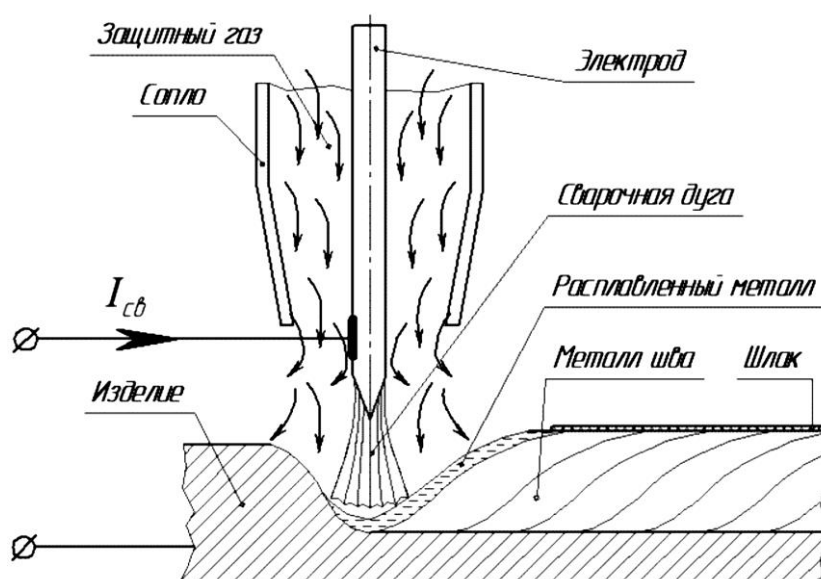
Схема аргонодуговой сварки неплавящимся электродом
